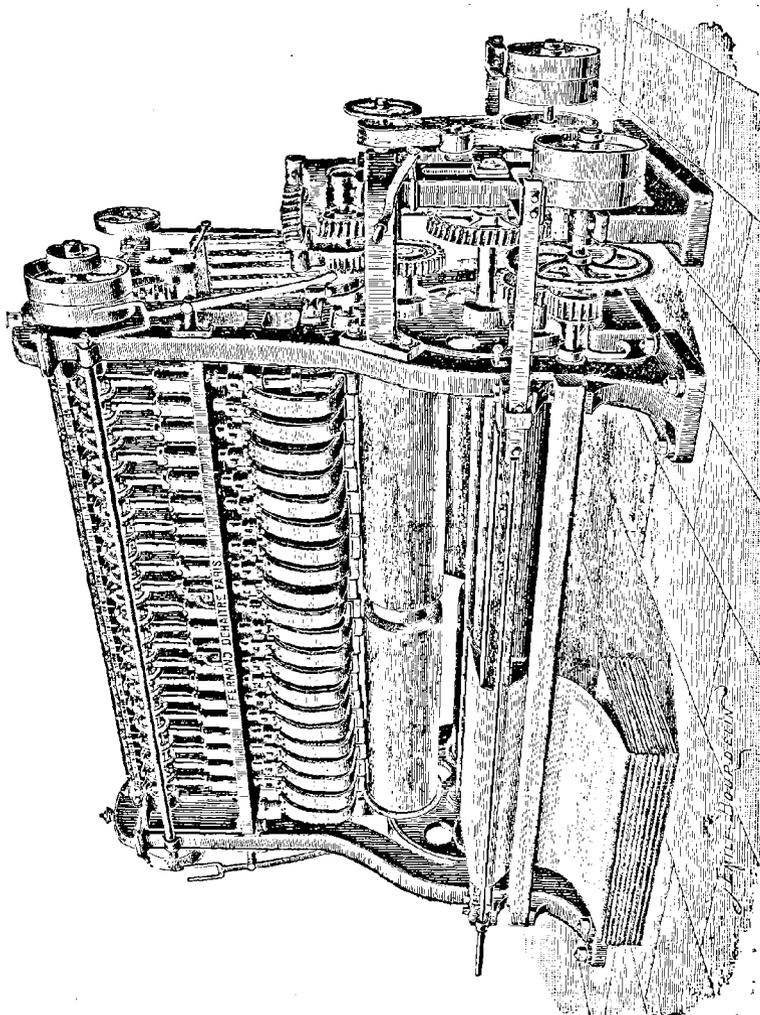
Beette à ressorts vue de devant. Dans cette machine, il n'y a que deux rouleaux dans le bas.
